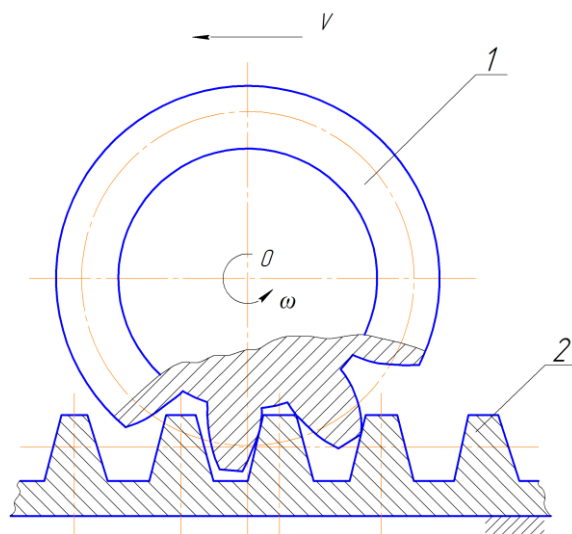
Реечная передача: 1 – зубчатое колесо; 2 – рейка
